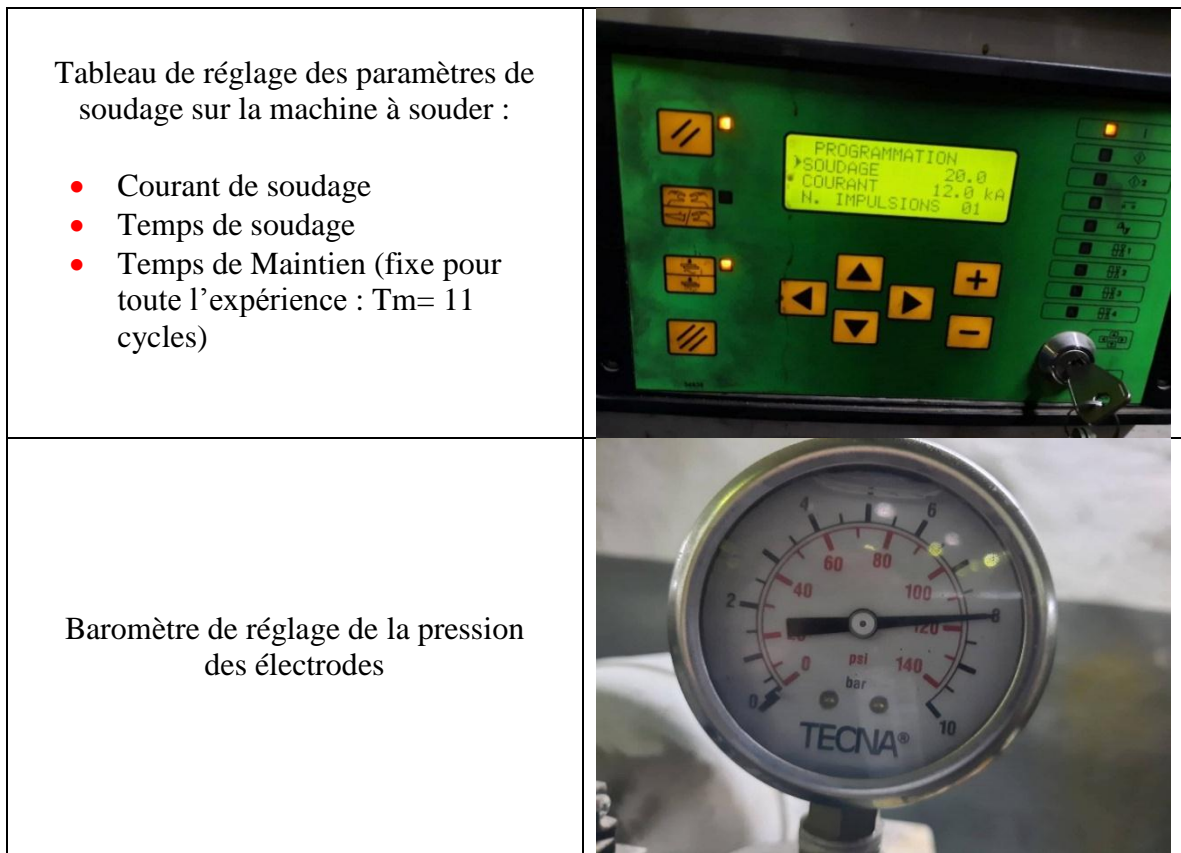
Réglage des paramètres de soudage sur la machine à souder.
